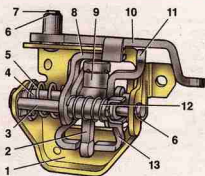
Механизм выбора передач: 1 — корпус механизма выбора передач; 2 — рычаг выбора передач (переднего хода); 3 — направляющая ось блокировочных скоб; 4 — ось рычага выбора передач; 5, 12 — пружина; 6 — стопорное кольцо; 7 — ось вилки заднего хода; 8, 13 — блокировочные скобы; 9 — фиксатор рычага выбора передач; 10 — вилка включения заднего хода; 11 — рычаг выбора передач (заднего хода)
